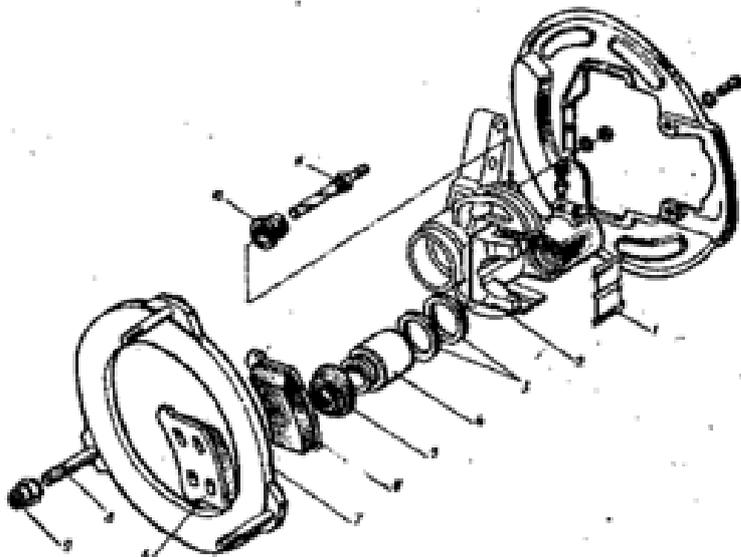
Детали переднего тормоза: 1 - пружина колодок; 2 - скоба тормоза; 3 - кольцо уплотнительное поршня; 4 - поршень; 5 - чехол защитный; 6 - колодка тормоза; 7 - диск тормоза; 8 - болт; 9 - гайка крепления колеса; 10 - чехол защитный пальца; 11 - палец направляющий.
